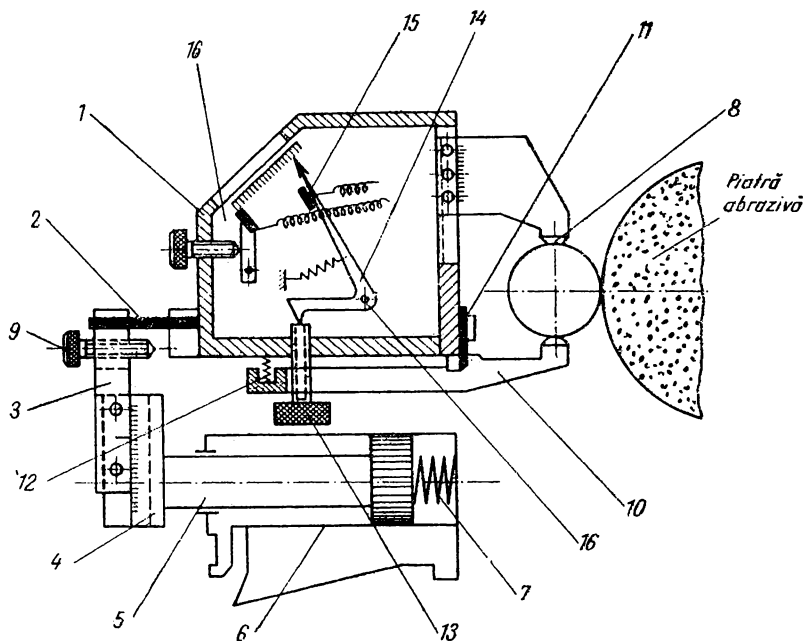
Mecanism de oprire automată cu traductor de dimensiune
